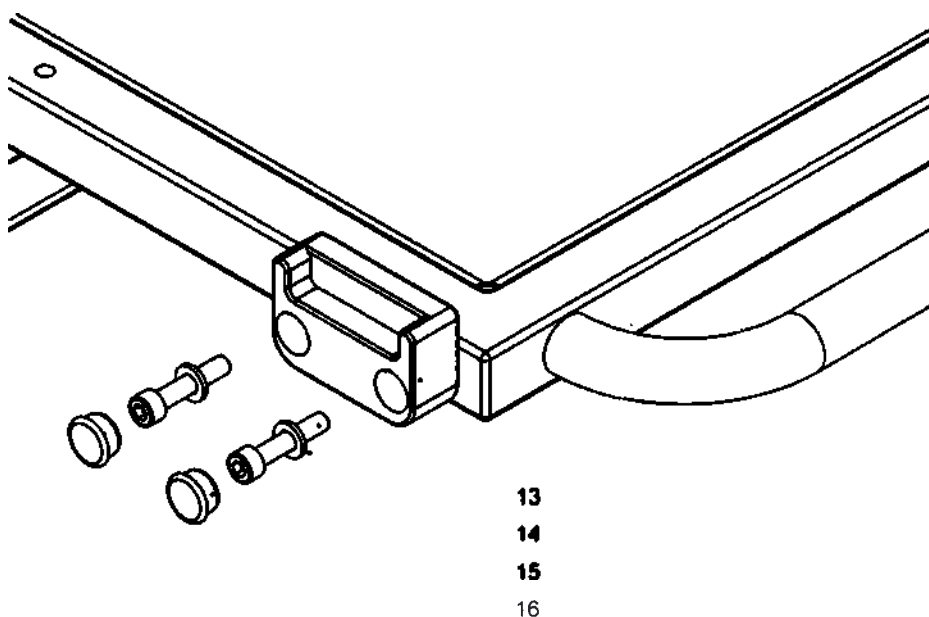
Схема установки опоры для крепления кронштейна К-3.
